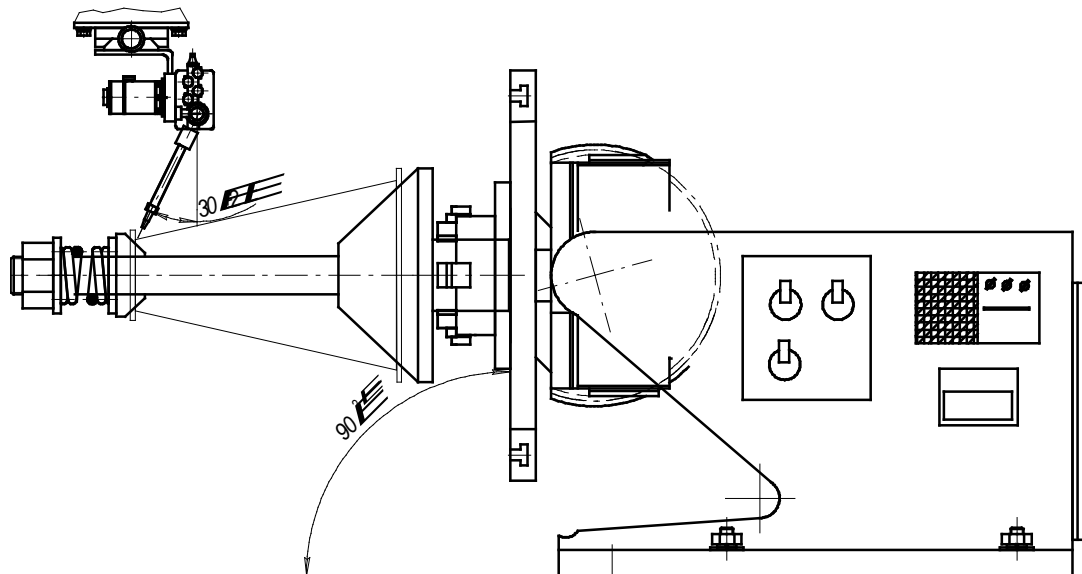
Схема настройки оборудования для сварки
